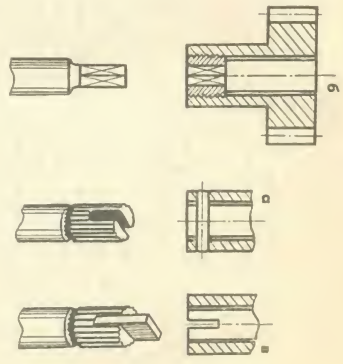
Способы соединения шестерни с валом: а — при помощи стержня; б — вставкой с резьбой; в — посредством пластины.
